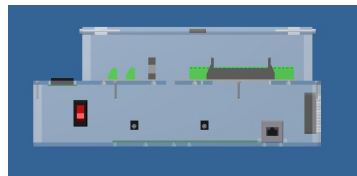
Vista frontal de la carcasa del registrador universal de datos
